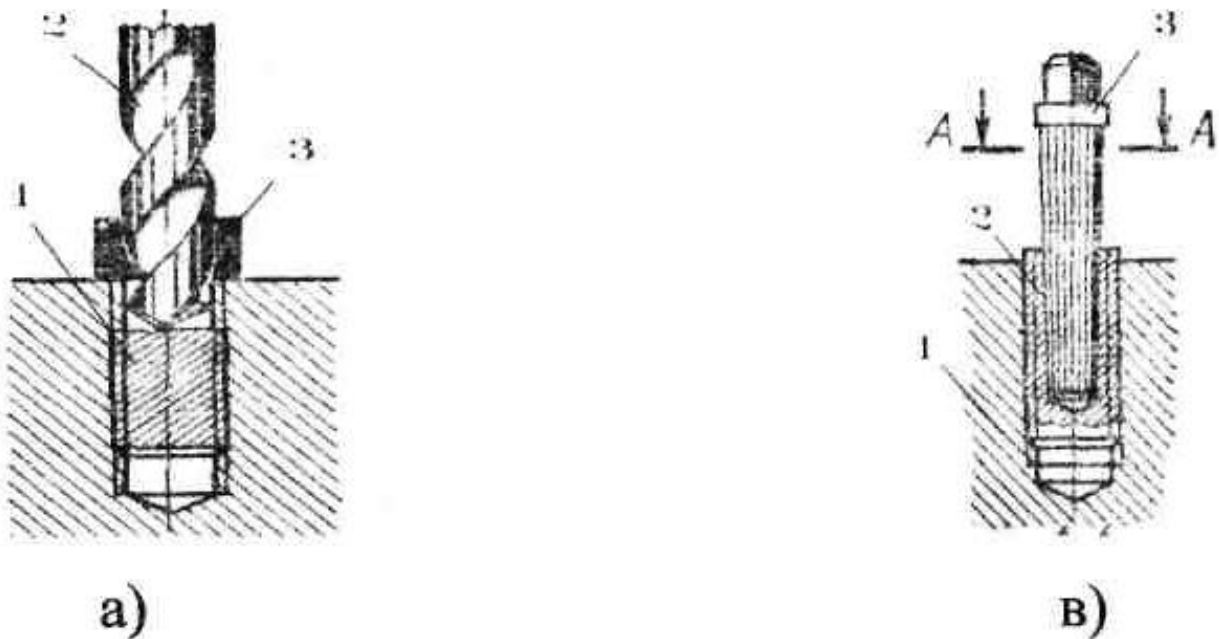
Видалення обірваної шпильки: а) висвердлювання по кондукторній втулці: 1- шпилька; 2- свердло; 3- кондукторна втулка; б) викручування шпильки циліндричним екстрактором: 1- циліндричний екстрактор; 2- шпилька; 3- деталь.
